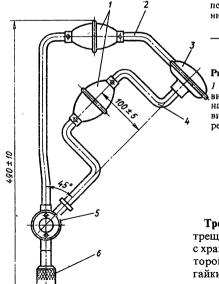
Универсальный коловорот: I — ручки; 2 — коленчатый неподвижный стержень; 3 — соединительная головка; 4 — коленчатый подвижный стержень; 5 — механизм передачи; 6 — патрон
